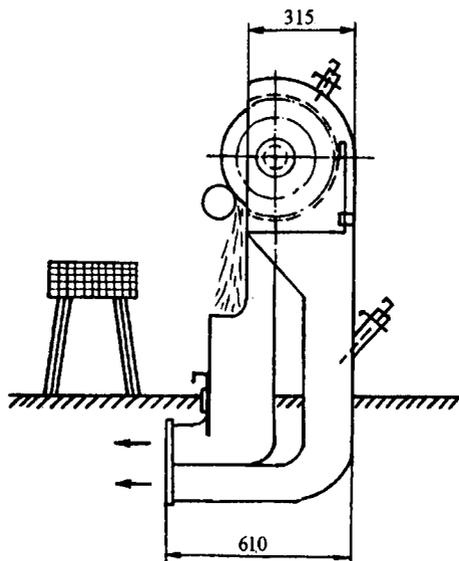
Защитно-обеспыливающий кожух заточного станка
